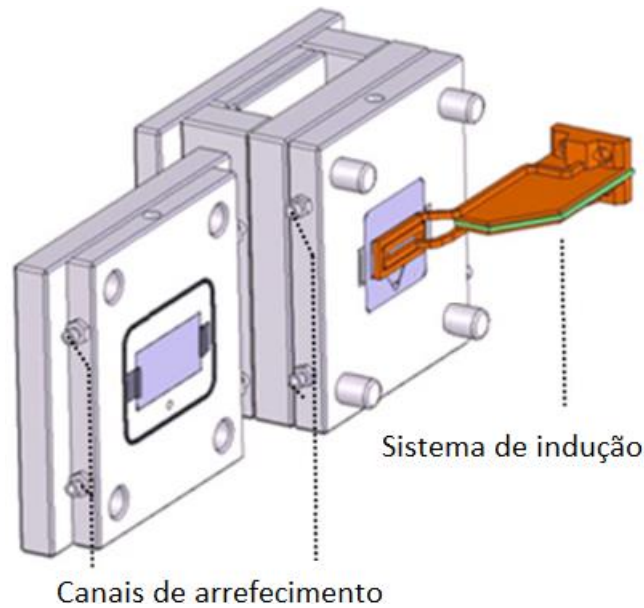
Molde com aquecimento por indução desmontado, adaptado de [23].
